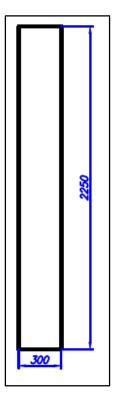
8 Dimensiones de las placas laterales. Fuente Autores.
